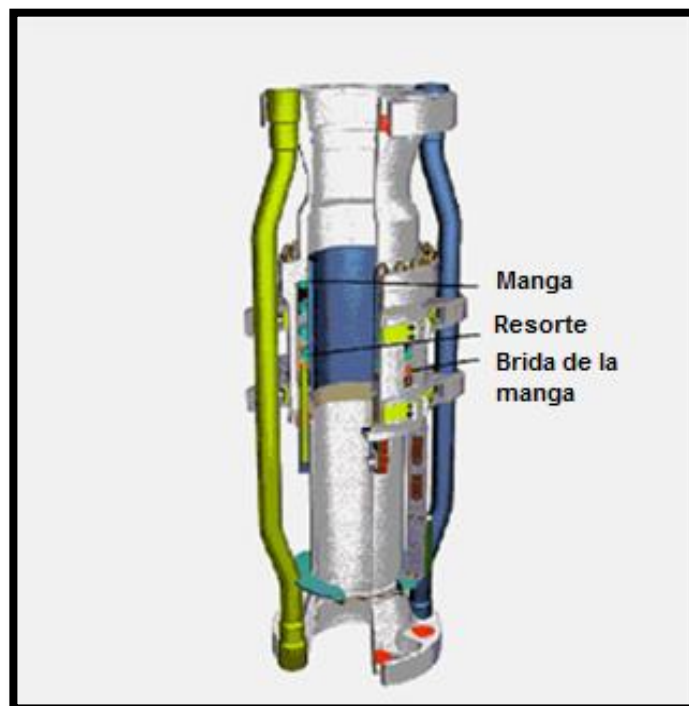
Válvula de autollenado del riser. [PEMEX]
